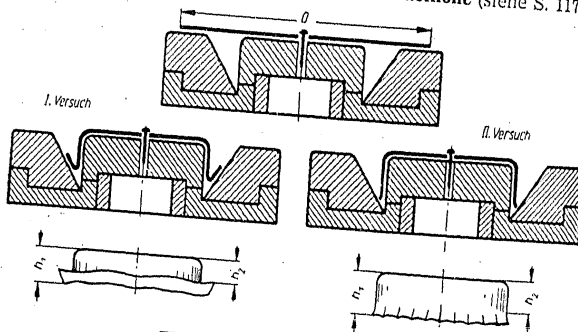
Kombiniertes Gummi-Preß- und -Schnittwerkzeug mit Auswerfer
